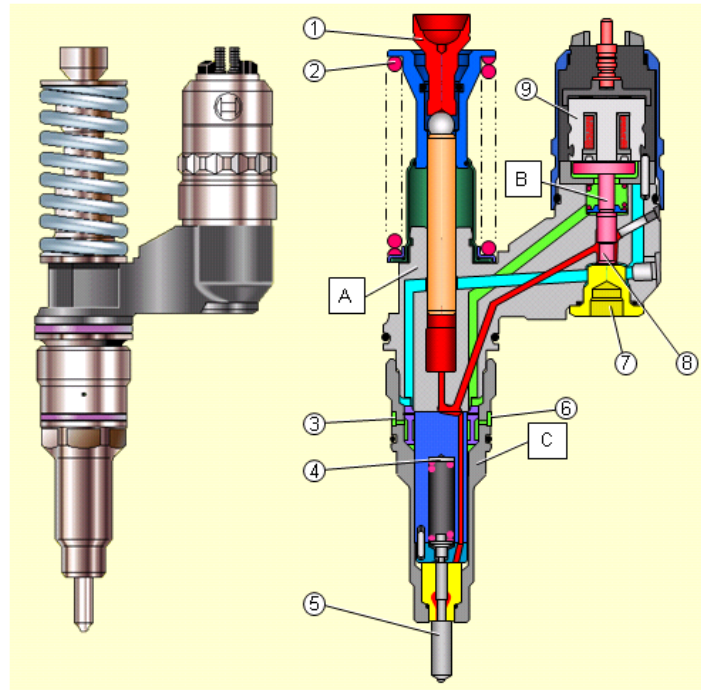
Схема насос-форсунки: 1- Пружина клапана, 2 - Форсунковий корпус, 3 - Направляючий елемент, 4 - Розпилювач, 5 - Канали подачі палива, 6 - Паливний шток (плунжер), 7 - Клапан високого тиску, 8 - Канали відведення надлишкового палива, 9 - Соленоїдний клапан.
